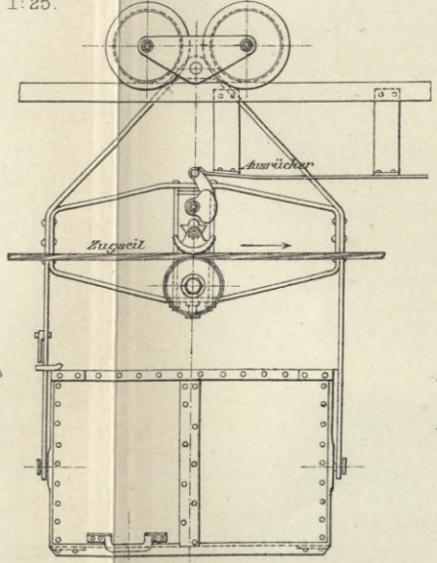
Gerüst an der Entladestelle.(Vorderansicht).
